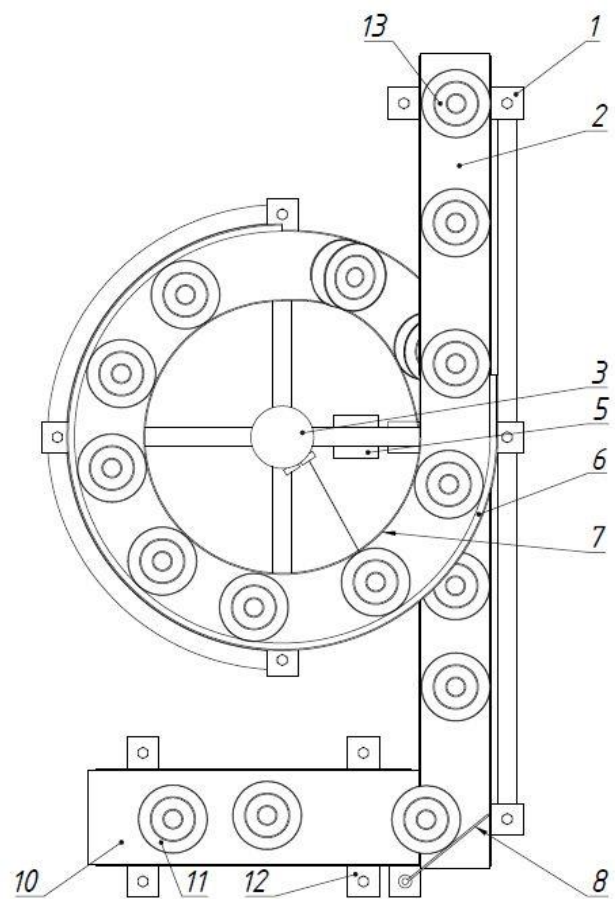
Устройство для контроля герметичности консервных банок, вид сверху
